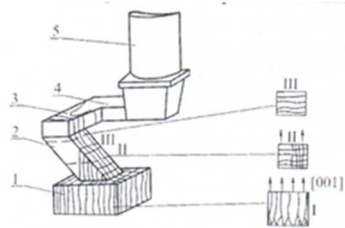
Схема ливарної форми для отримання монокристалічного виливка від затравки
